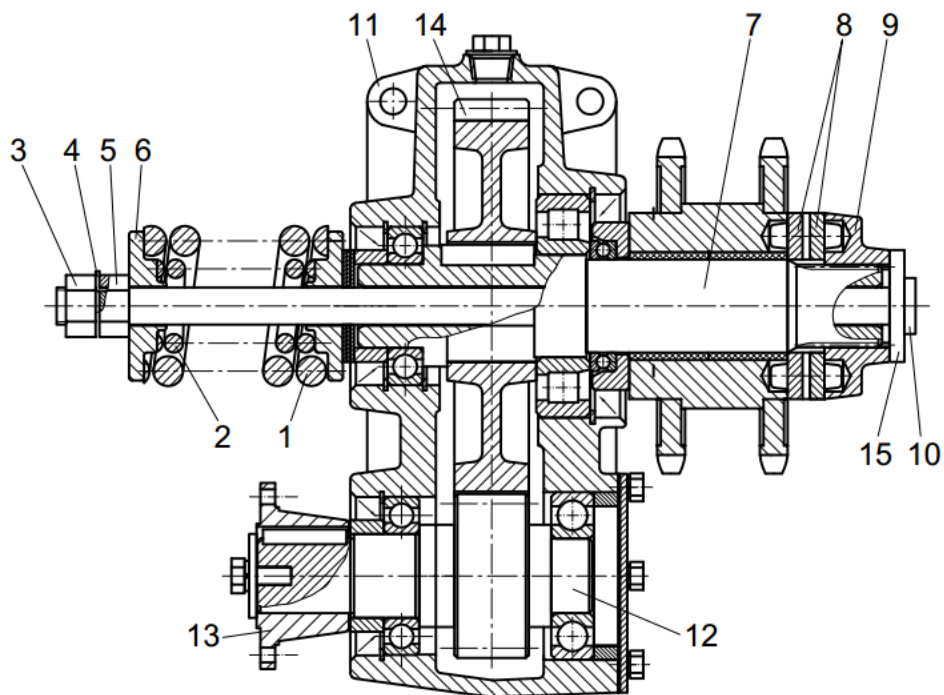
Редуктор верхній приводу шнеків КС6В-48.010
